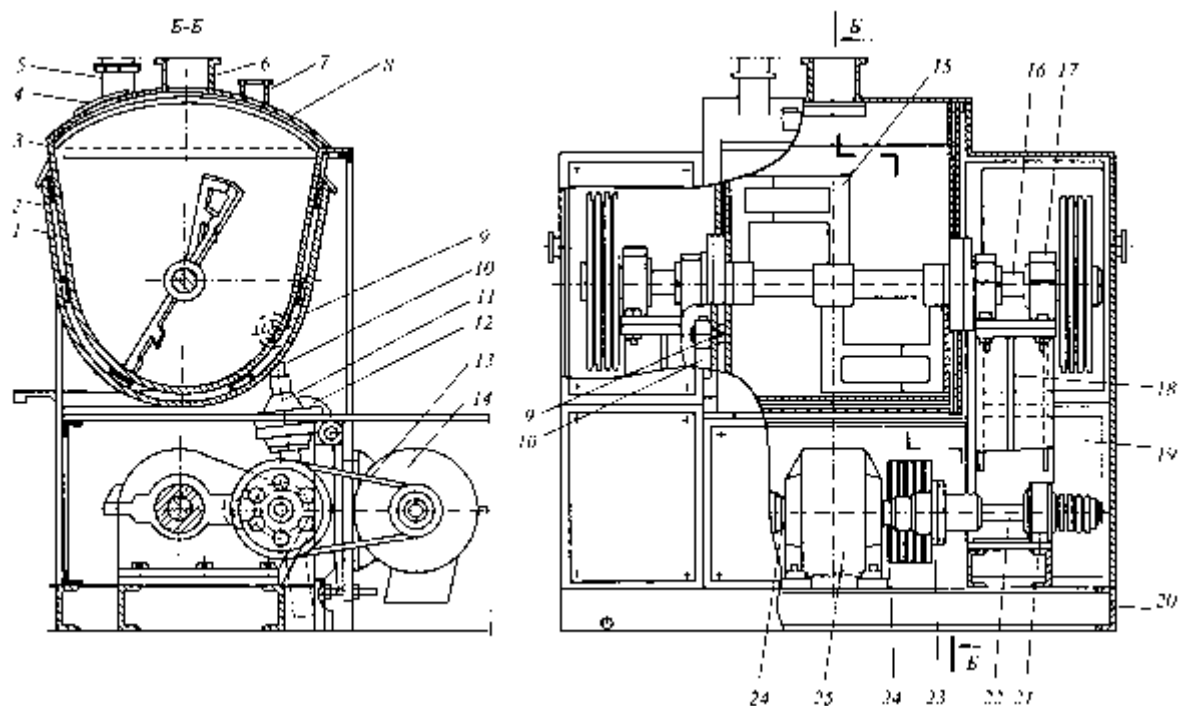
Конструктивная схема тестомесильной машины с горизонтальным месильным валом: 1 - рубашка; 2 - изоляция; 3 - емкость; 4 - откидной люк; 5 - патрубок для фильтра; 6,7 - загрузочные патрубки; 8 - неподвижная крышка; 9 - шарнир; 10 - шток; 11, 25 - редукторы; 12, 14 - электродвигатели; 13 - клиноременная передача; 15 - месильная лопасть; 16 - месильный вал; 17, 21 - корпуса подшипников; 18 - стойка; 19 - цепная передача; 20 - станина; 22 - промежуточный вал; 23 - муфта; 24 - двухсторонний выходной вал редуктора
